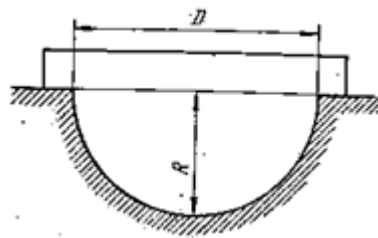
Вимірювання форми контрольних розточок.
